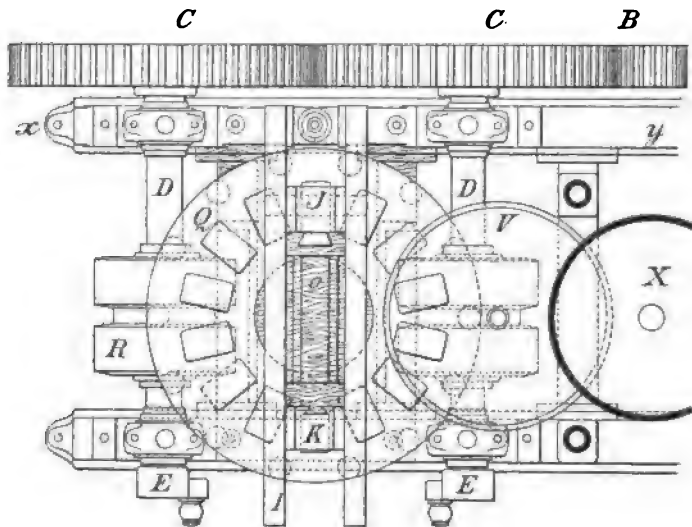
Couffinal's Presse, Grundriss.
